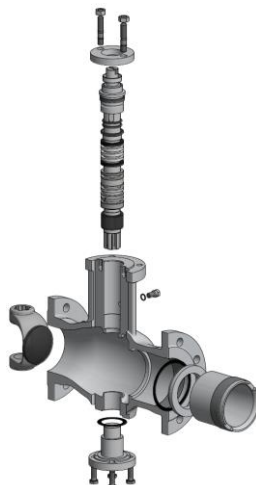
Explosionszeichnung • Ventil Typ 72.3 Standard
